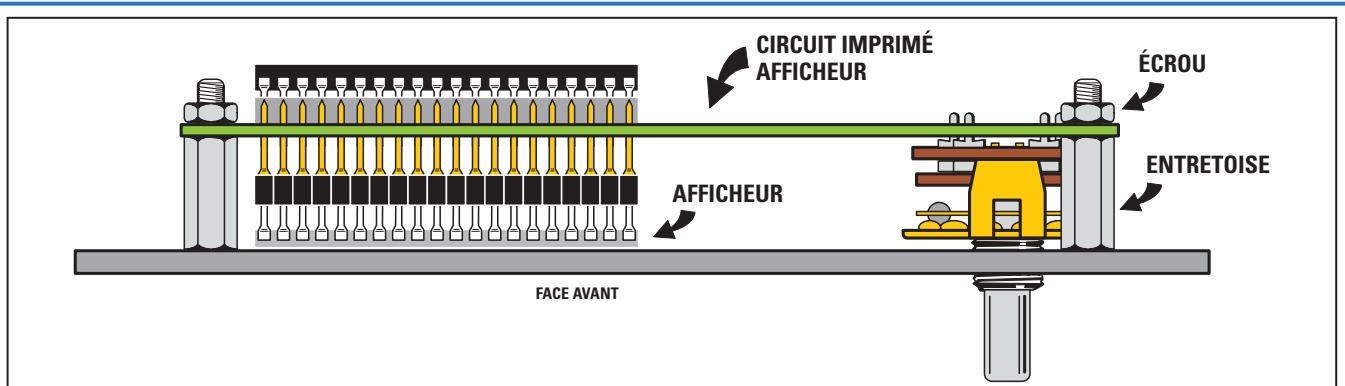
Après avoir fixé le circuit imprimé sur la face avant, jouez sur l'enfoncement des 2 supports tulipes du LCD de telle manière que ce dernier vienne bien s'appuyer derrière sa fenêtre de face avant. C'est alors seulement que vous pourrez souder les broches des supports tulipes du LCD puis couper ce qui dépasse des soudures.
